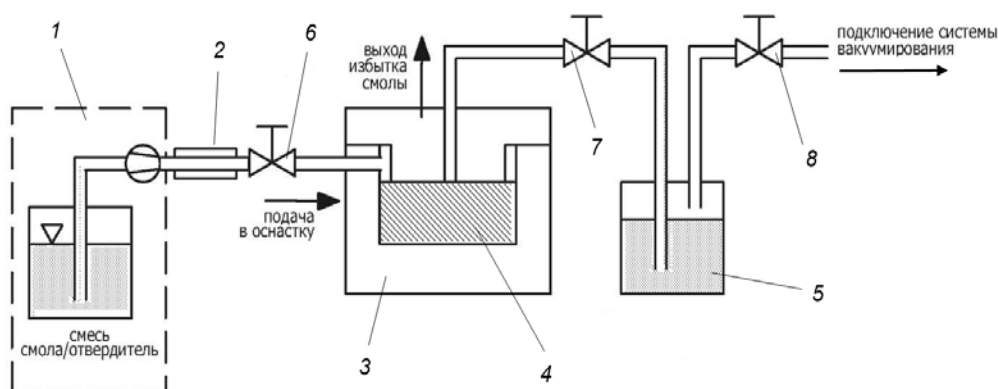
Технологическая схема процесса RTM (1 – подача смолы; 2 – обогреваемая трубка; 3 – оснастка; 4 – заготовка детали; 5 – ловушка; 6 – инжекционный клапан; 7 – выпускной клапан; 8 – вакуумный клапан)
